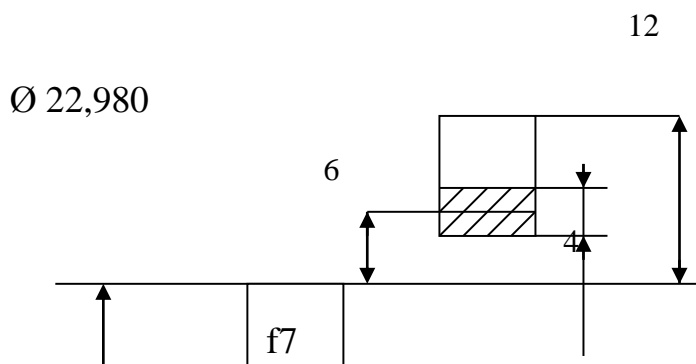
Расположение полей допусков калибр-кольца для размера $\varnothing 23f7$
